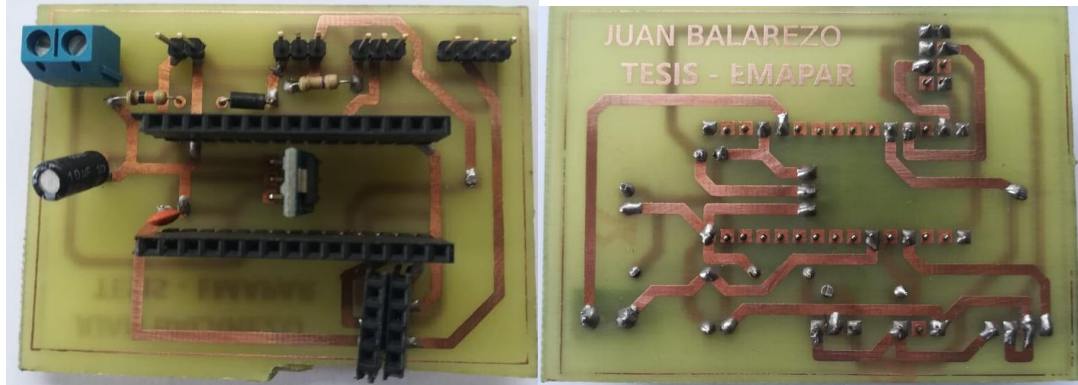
Placa electrónica nodo inalámbrico soldado
